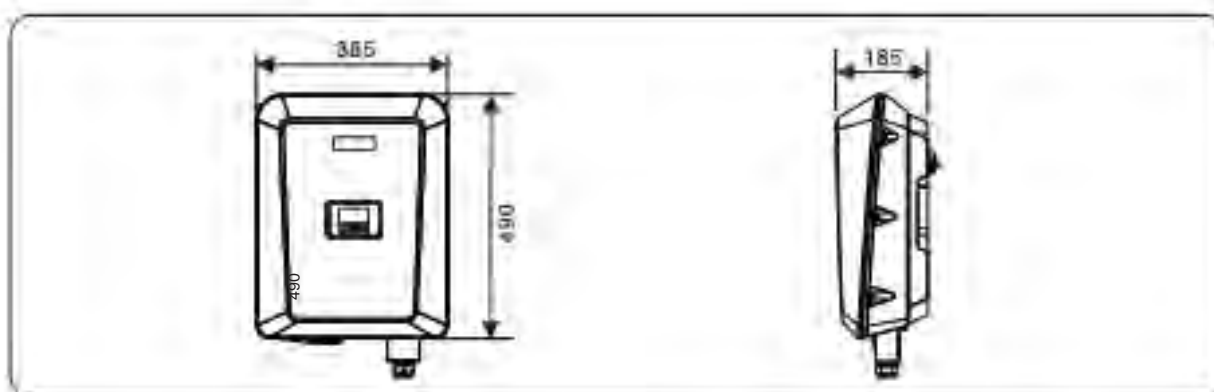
Dimensioni dell'inverter in vista frontale e laterale (unità: mm)
